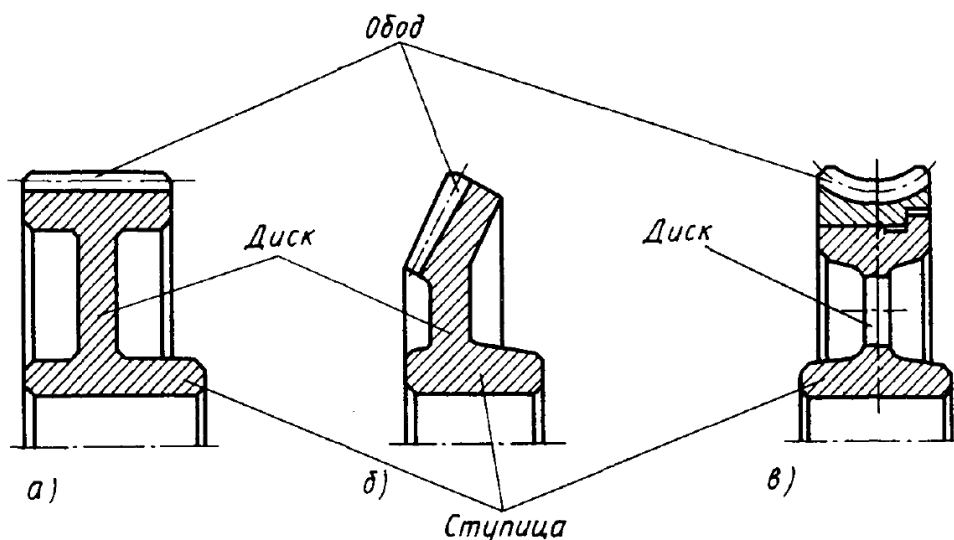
Основные конструкции цилиндрических зубчатых колёс
